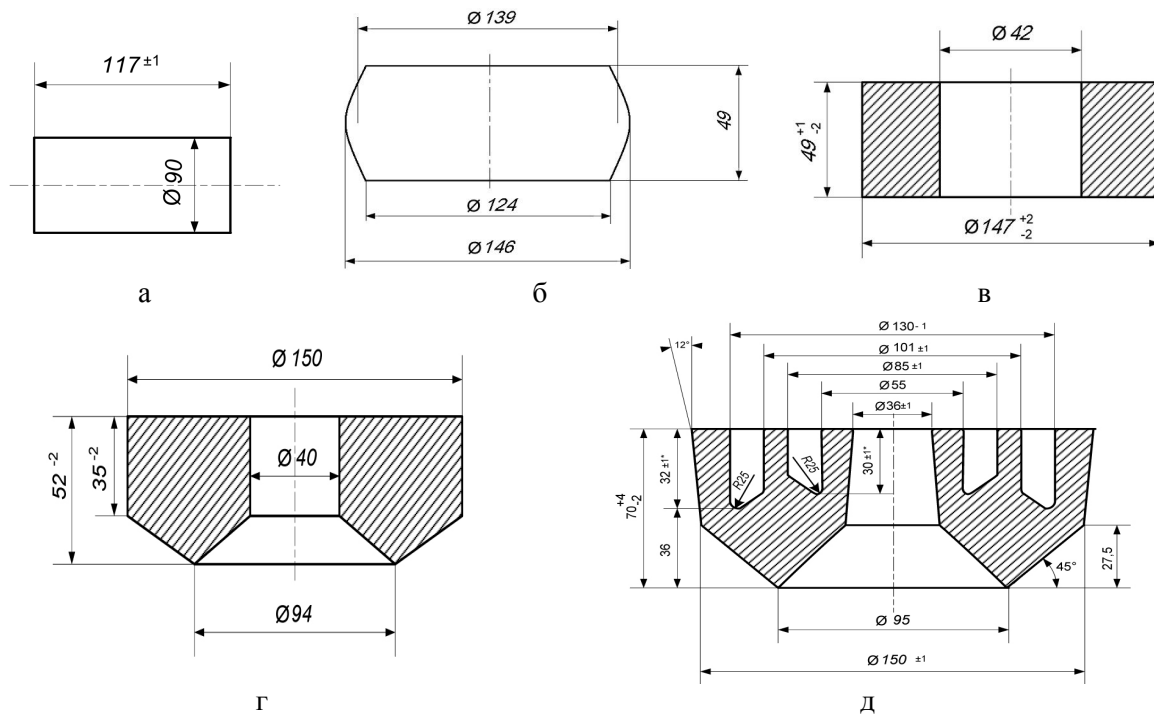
Эскизы переходов штамповки поковки «Головка кислородной фурмы»: а – мерная заготовка, б – заготовка после осадки, в – заготовка после прошивки, г – поковка после предварительного рудья, д – поковка после окончательного рудья
